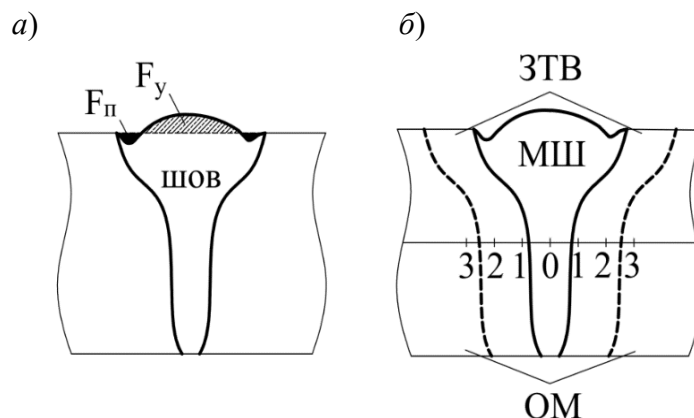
Схема формирования сварного шва (а) и зон индентирования (б): ОМ – основной металл; ЗТВ – зона термического влияния; МШ – металл шва
